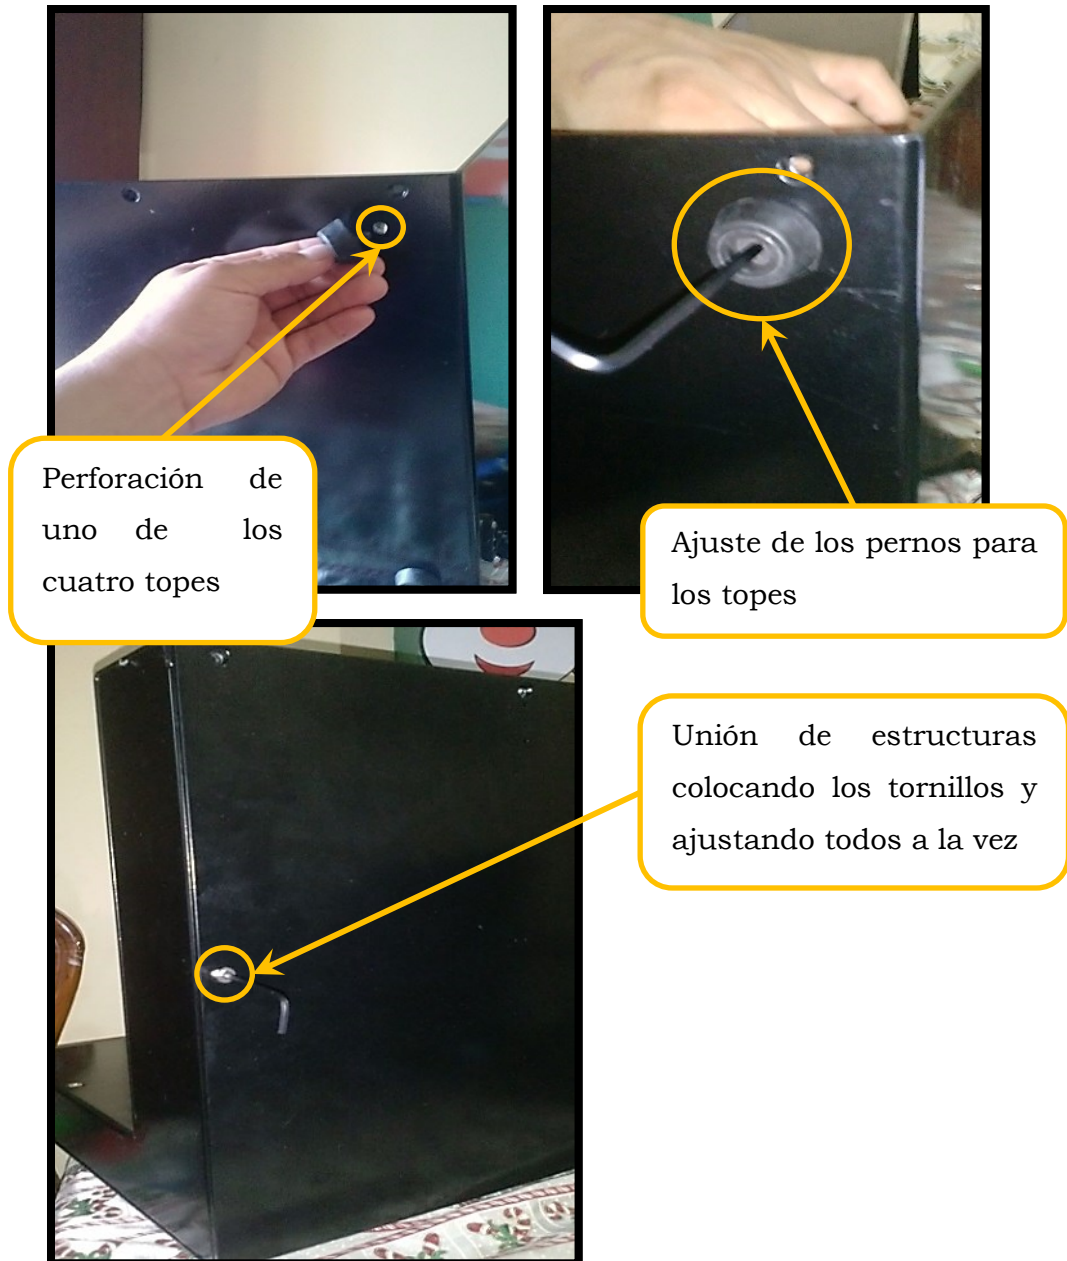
Montaje de topes y cierre de la estructura.
